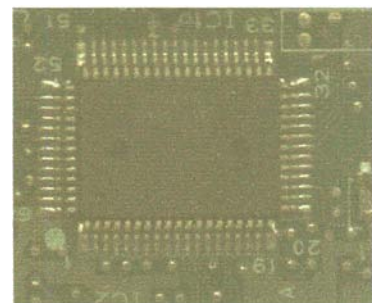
C - Imagem, obtida com um scanner, de um outro circuito integrado, mais complexo do que o TDA2003, soldado em uma placa de circuito impresso.
